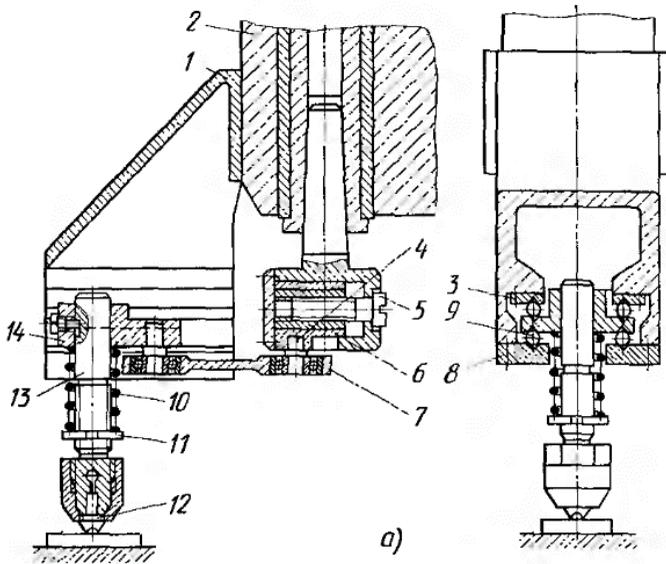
Конструкція віброголовки для обробки плоских поверхонь
